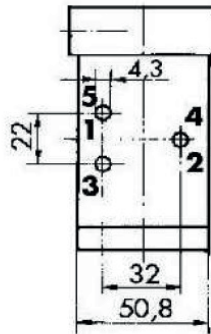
Verstärkerventil mit Durchgangsbohrung (Abmessungen in mm)
